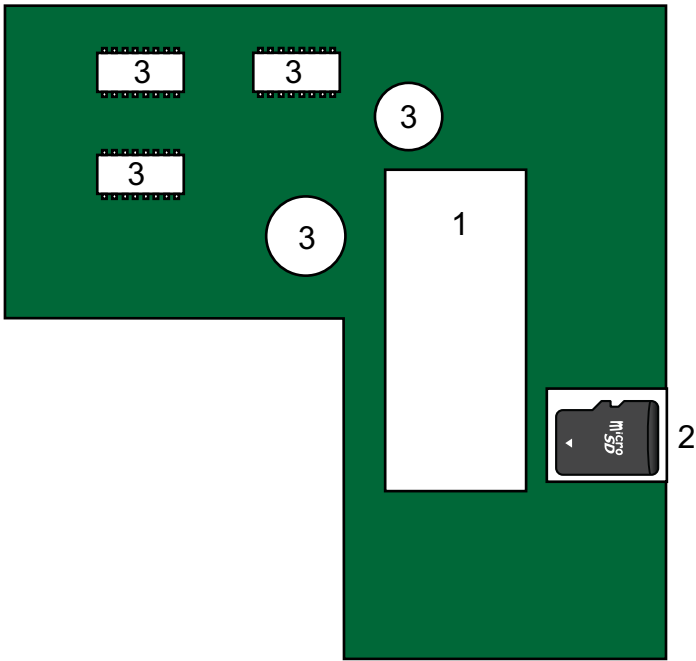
PACE E 시리즈 메인 PCB 의 일반 모습
